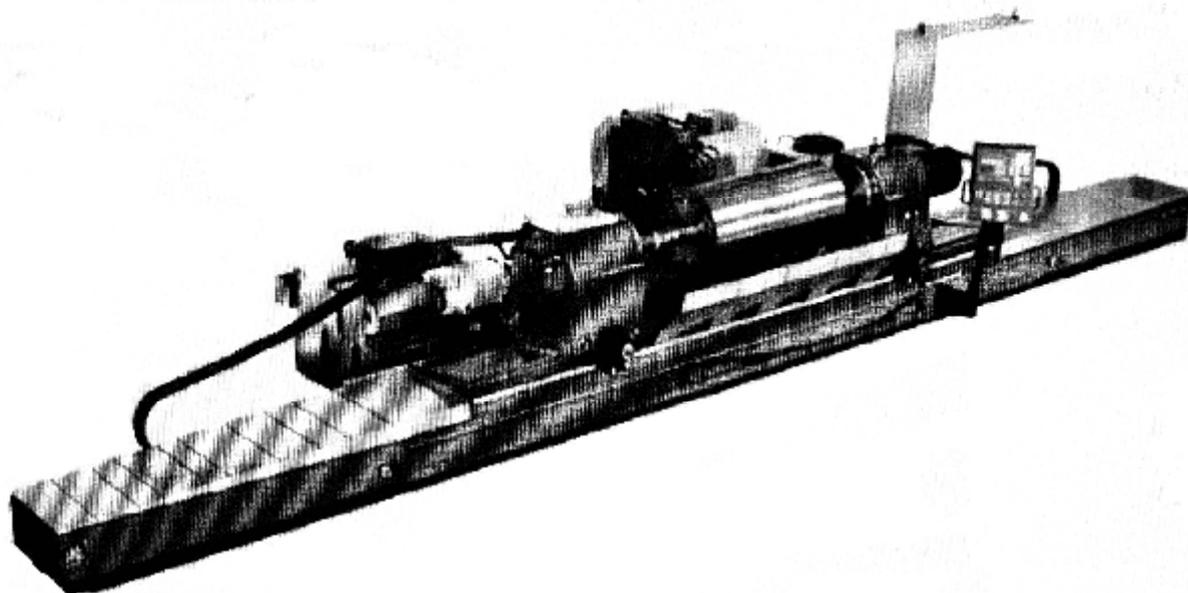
Круглошлифовальный станок CNC Heavy Duty с ЧПУ для обработки тяжелых деталей
